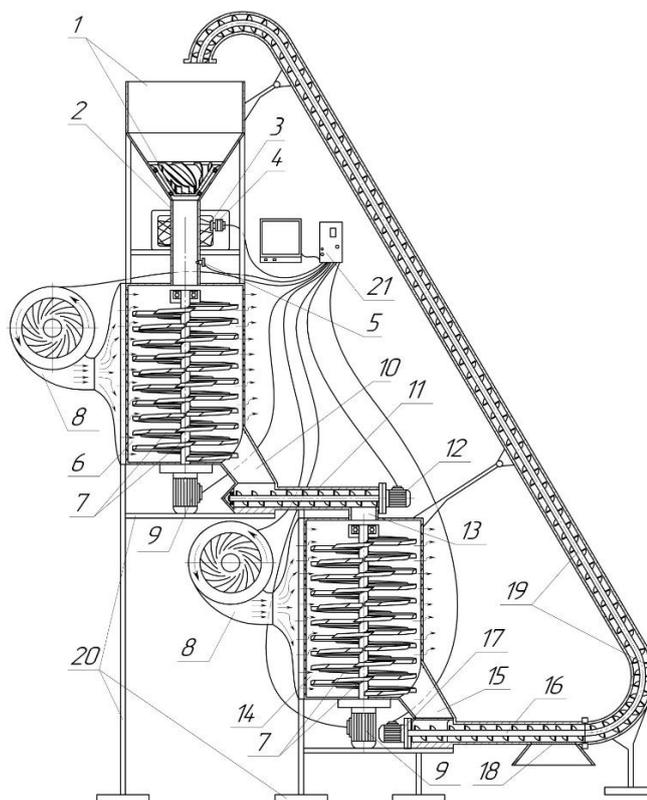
Конструктивна схема розробленої мікрохвильової сушильної установки: 1– бункер з механізмом розпушування сипкого матеріалу; 2 – діелектричний патрубок; 3 – камера надвисокочастотного (НВЧ) нагріву; 4 – магнетрон з НВЧ–резонатором; 5 – термодатчик; 6 – камера (бункер) попереднього охолодження; 7 – гвинтові робочі органи для змішування та розпушування сипкого матеріалу; 8 – вентилятори; 9 – електроприводи гвинтових робочих органів для змішування та розпушування сипкого матеріалу; 10, 13, 15 – перевантажувальні патрубки; 11 – шнековий дозатор; 12 – електропривід шнекового дозатора з електронним керуванням; 14 – камера (бункер) кінцевого охолодження; 16 – вивантажувальний шнек; 17 – електропривід вивантажувального шнека; 18 – розвантажувальний отвір з шибром; 19 – перевантажувальний гнучкий шнек; 20 – опорно–руховий механізм; 21 – блок управління елементами установки
